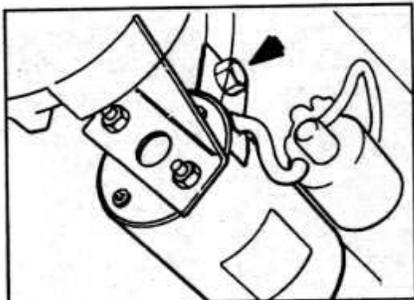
А.23. Расположение болта крепления подвески поддержки стартера.
